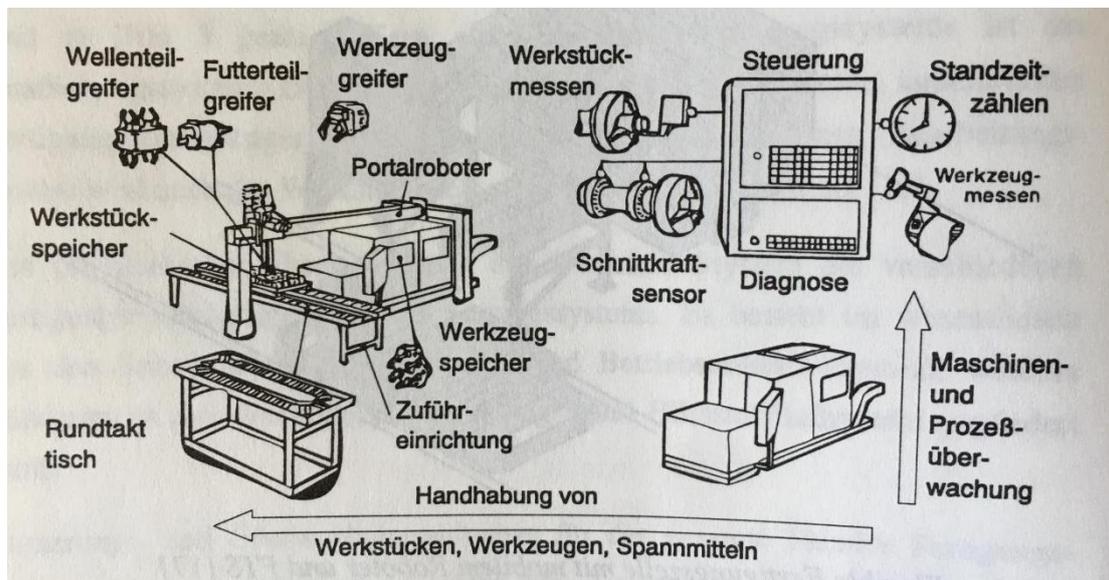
Automatisierung von Werkzeugmaschinen ^[1]
